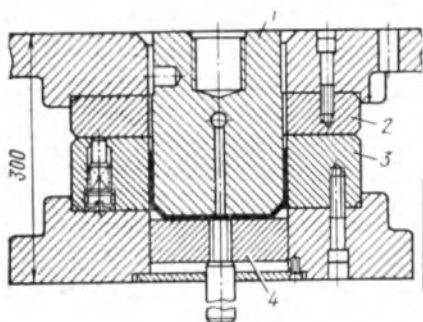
Вытяжной штамп для прессы двойного действия
